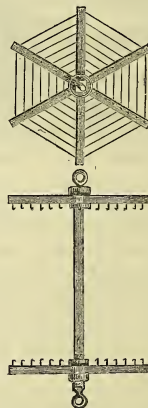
Cadre ou *champagne*, pour la teinture des calicots.
